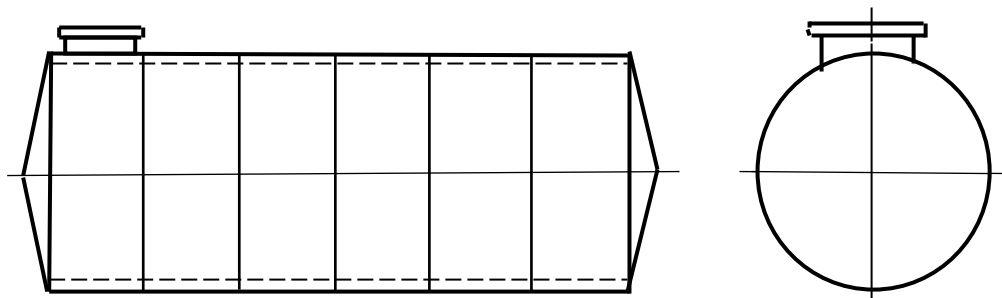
Эскиз конструкции резервуара РГС – 75 зав. №111
